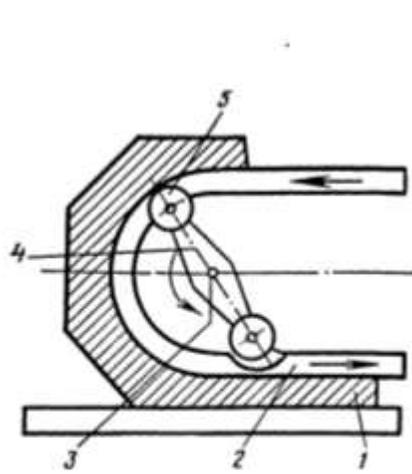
Схема шлангового насоса: 1 — станина; 2 — шланг; 3 — подшипник; 4 — планка; 5 — ролик
